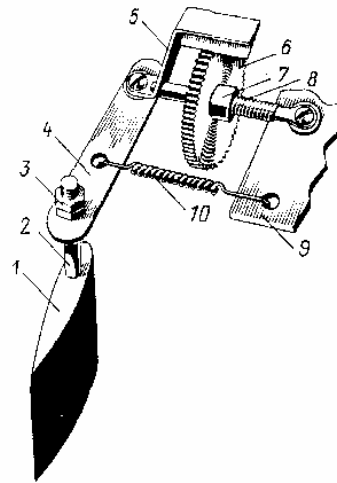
Конструкция привода руля с точной регулировкой.
